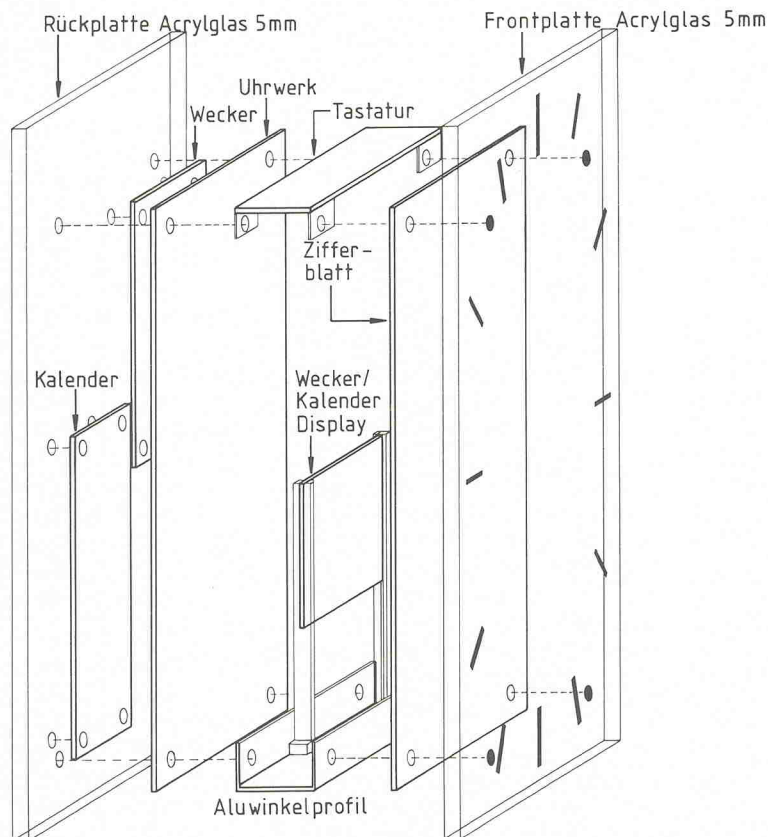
Die hier abgebildete Explosionszeichnung erleichtert die korrekte Montage aller Uhrenmodule.
